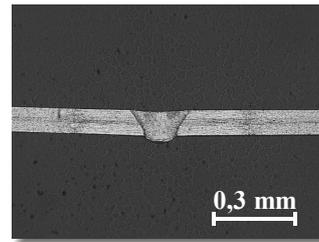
Querschliff einer Blindschweißung in ein 0,1 mm dickes Edelstahlblech ( $v = 3 m/min$ )
